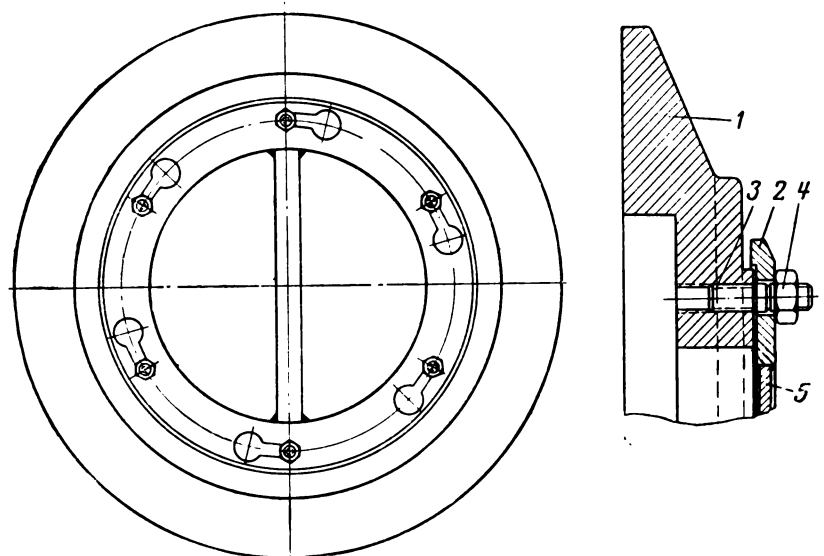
Оправка для выдавливания чашки вентилятора
